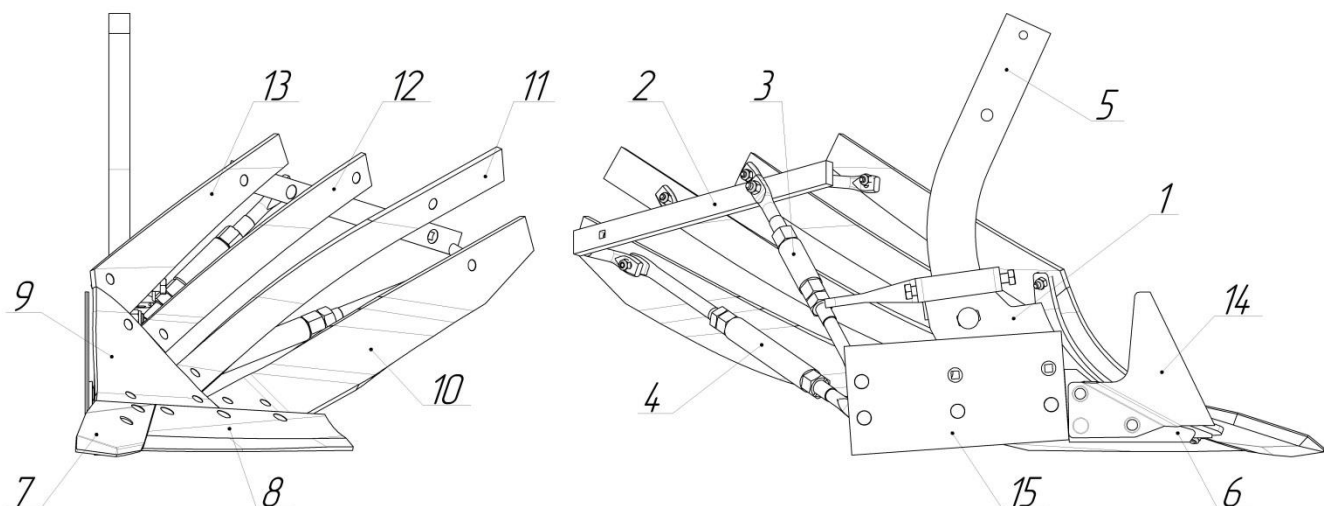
Корпус ПО-40.000 (левооборачивающий)
